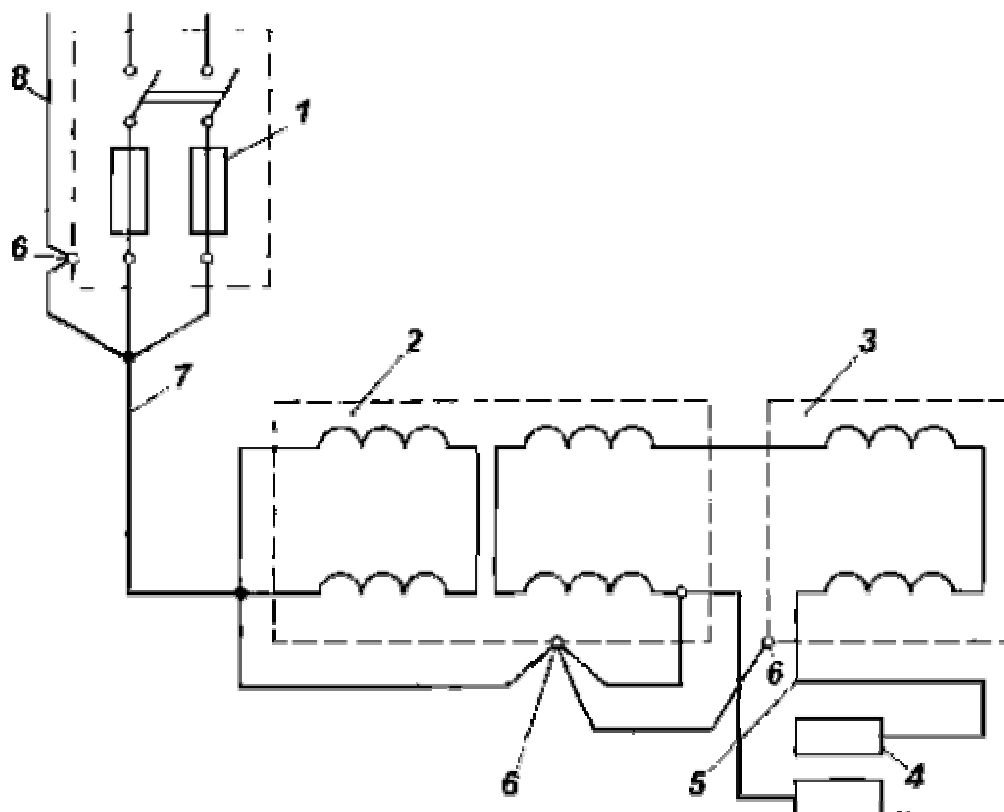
Схема подключения сварочного трансформатора: 1 — пункт питания; 2 — сварочный трансформатор; 3 — регулятор; 4 — электрододержатель; 5 — шланговый одножильный провод; 6 — заземляющий болт; 7 — питающий шланговый трехжильный кабель с заземляющей жилой; 8 — нулевой провод сети.
